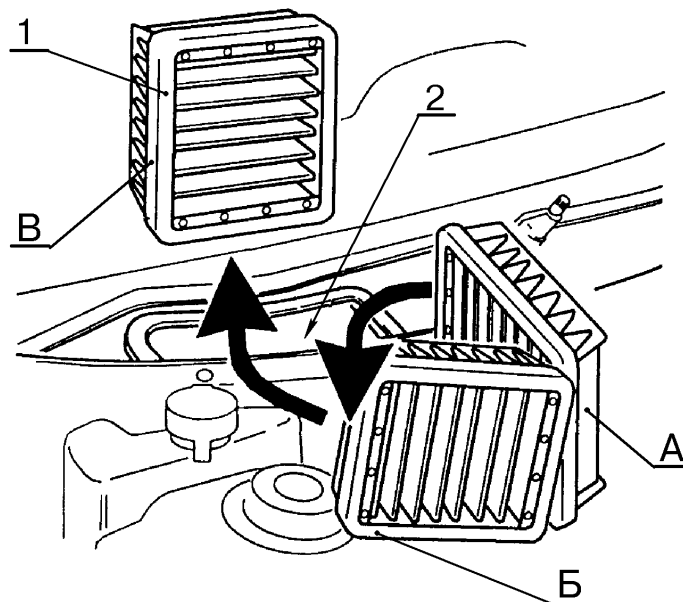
Снятие и установка воздушного фильтра системы вентиляции и отопления салона.
